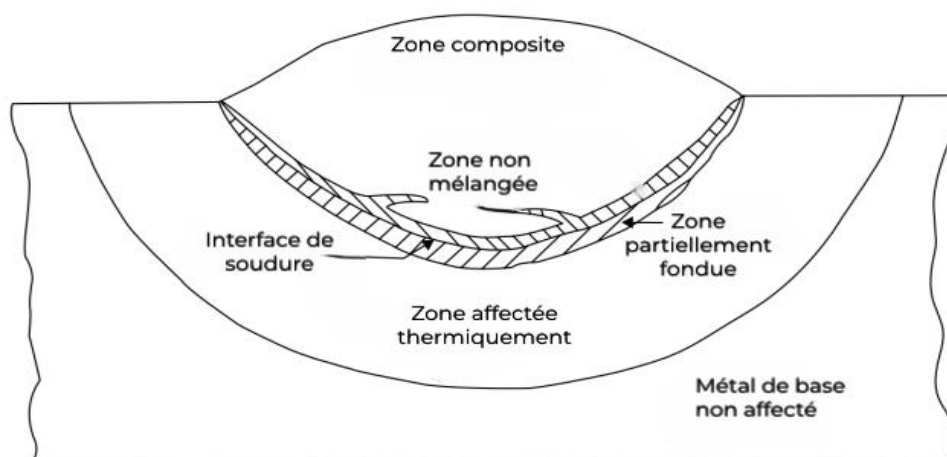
Les zones de soudure en 1976. [3]
